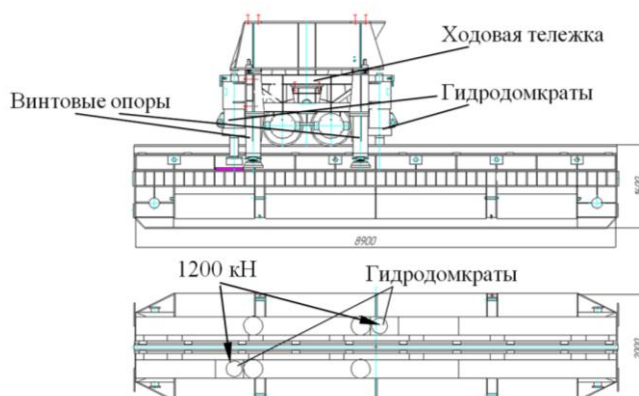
Опорная балка с ходовой тележкой, гидродомкратами и винтовыми опорами
